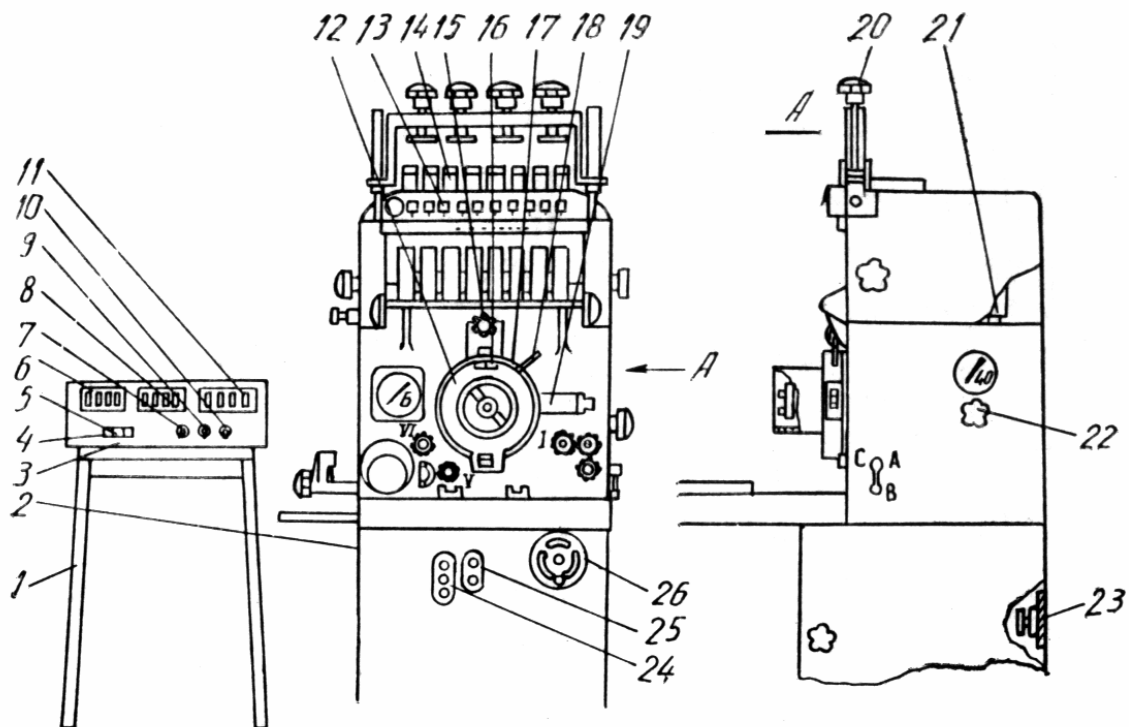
Контрольно-измерительный стенд КИ-22205:
